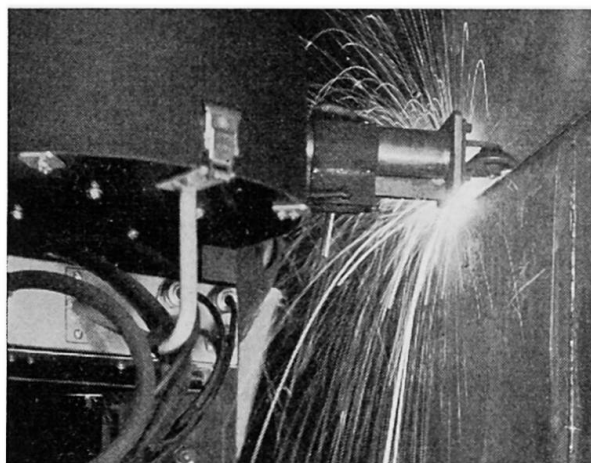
Vollautomatisches Schweißen einer Horizontalnaht (Detailaufnahme).
